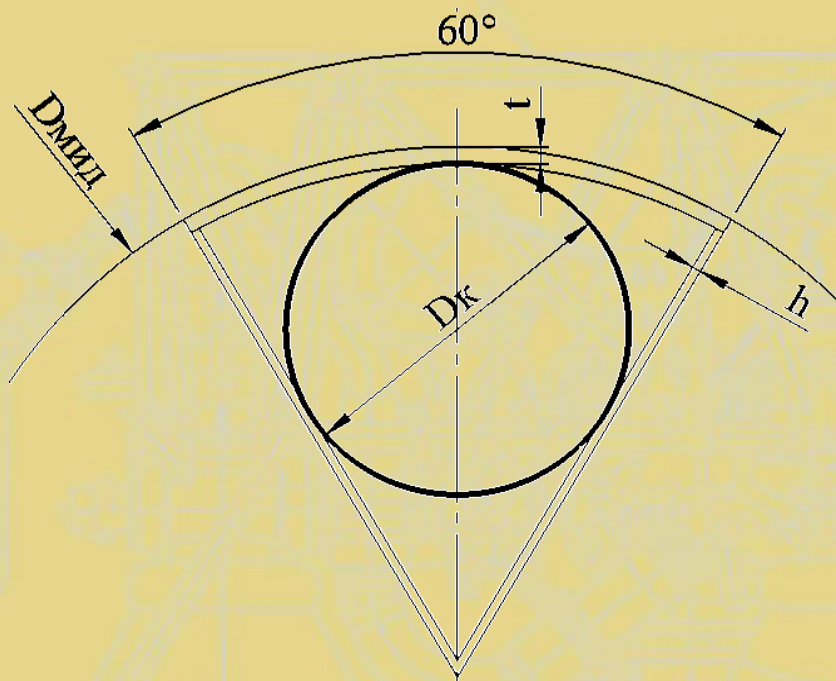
Предварительная прорисовка поперечного заполнения корпуса ЛА
